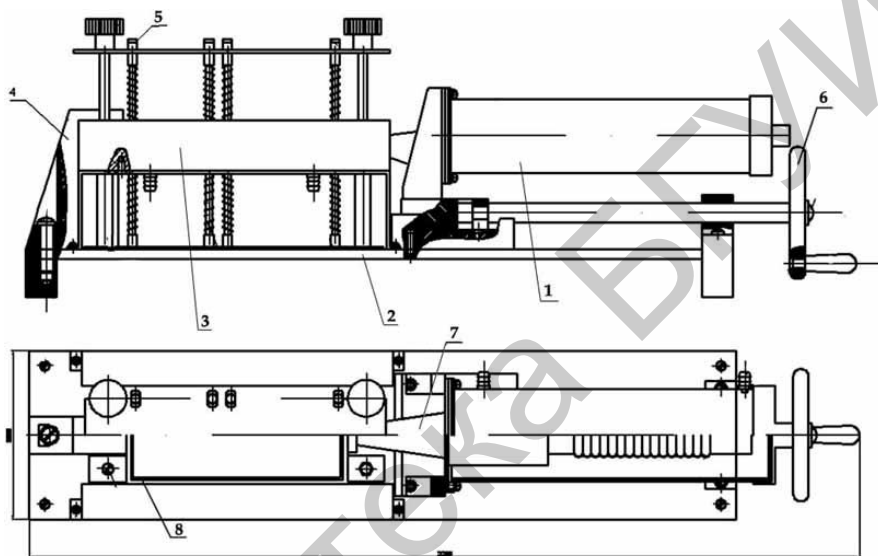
Устройство ультразвуковой пайки микроплат в корпус модуля
